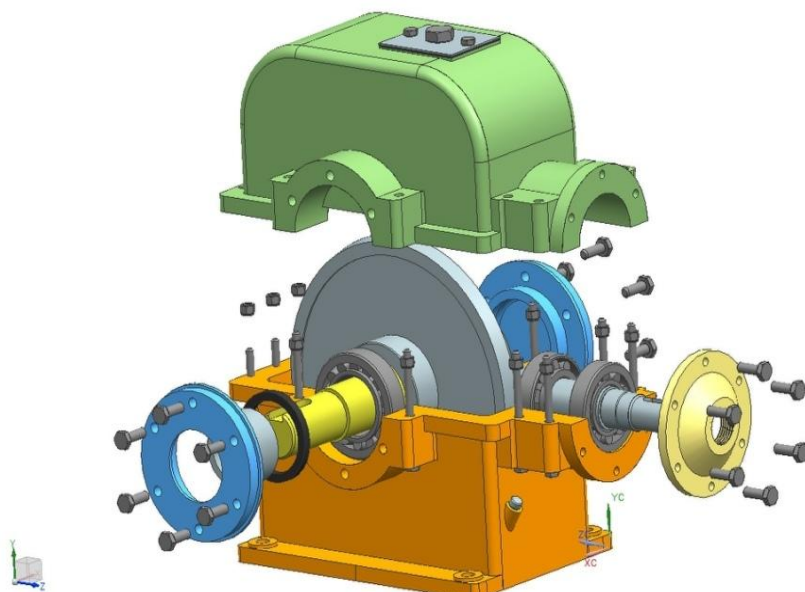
Одноступенчатый конический редуктор (составляющие)
